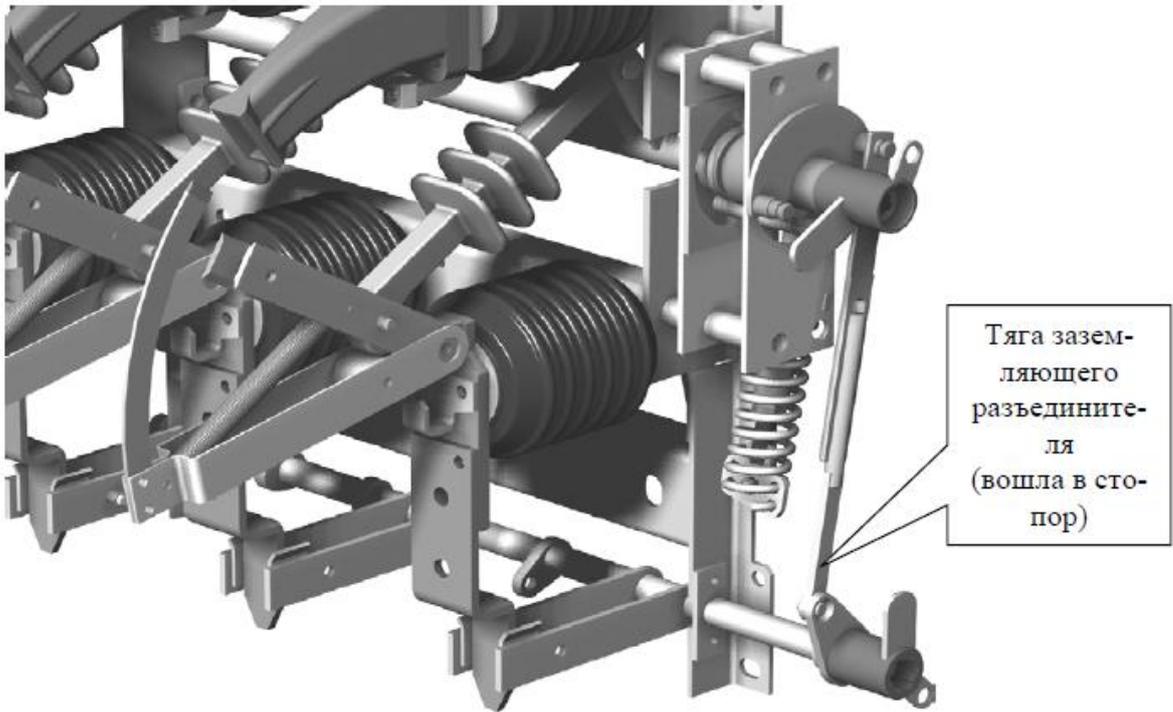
Блокировка выключателя нагрузки и заземляющего разъединителя (выключатель нагрузки отключен, заземляющий разъединитель включен).
